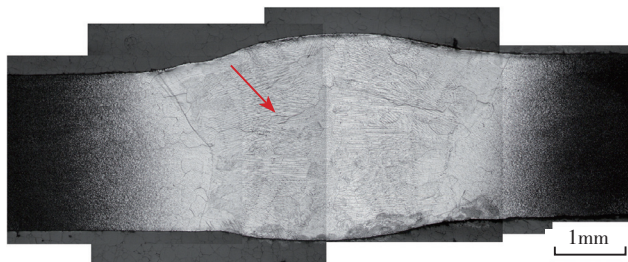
所示为传统TIG焊接和活性剂TIG焊接焊后焊缝形貌。图3(a)所示为传统TIG焊接焊后焊缝形貌,图中红圈位置所示为焊接接头的气孔,位于焊缝靠近熔合线的位置;图中箭头所示为焊缝区域柱状晶形貌,可见柱状晶沿垂直于熔合线方向生长,熔合线方向与母材呈较大的角度。未添加活性剂时,焊缝深度和宽度之比(深宽比)为0.24,焊缝区域呈现浅宽型,且焊接接头底
